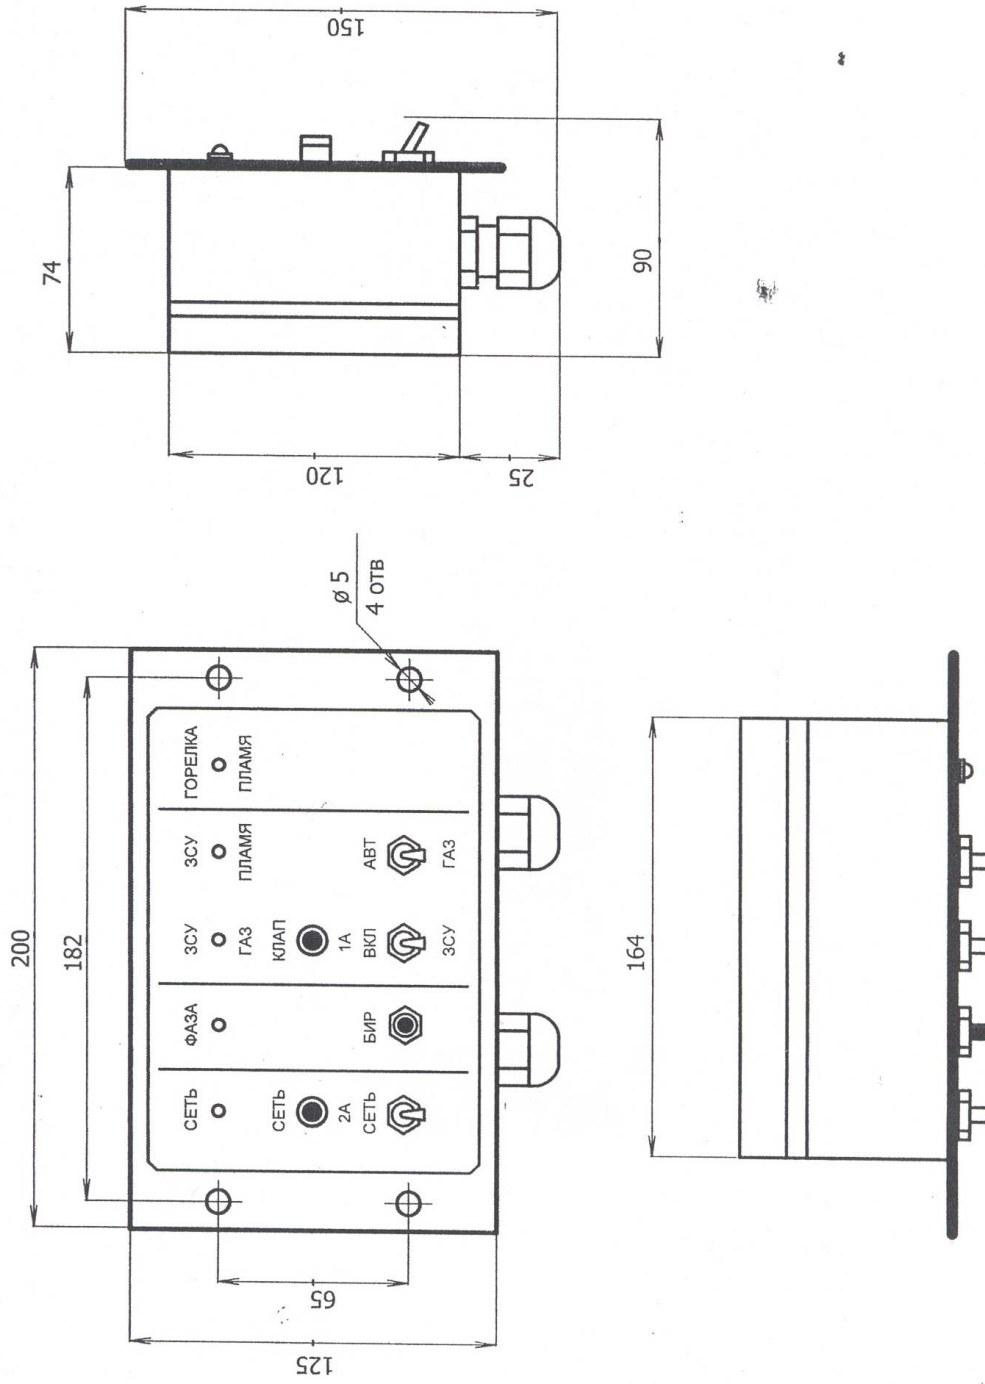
Габаритные и присоединительные размеры блока МЩУ-2.
